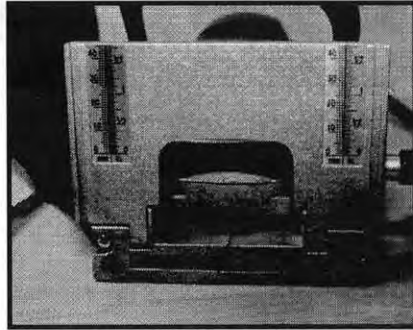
Enlèvement des vis horizontales pour démontage d'une JS102
